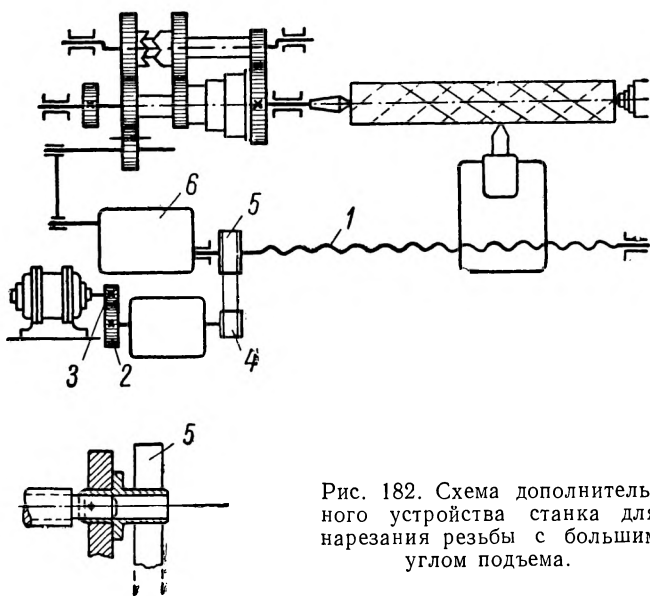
Схема дополнительного устройства станка для нарезания резьбы с большим углом подъема.
